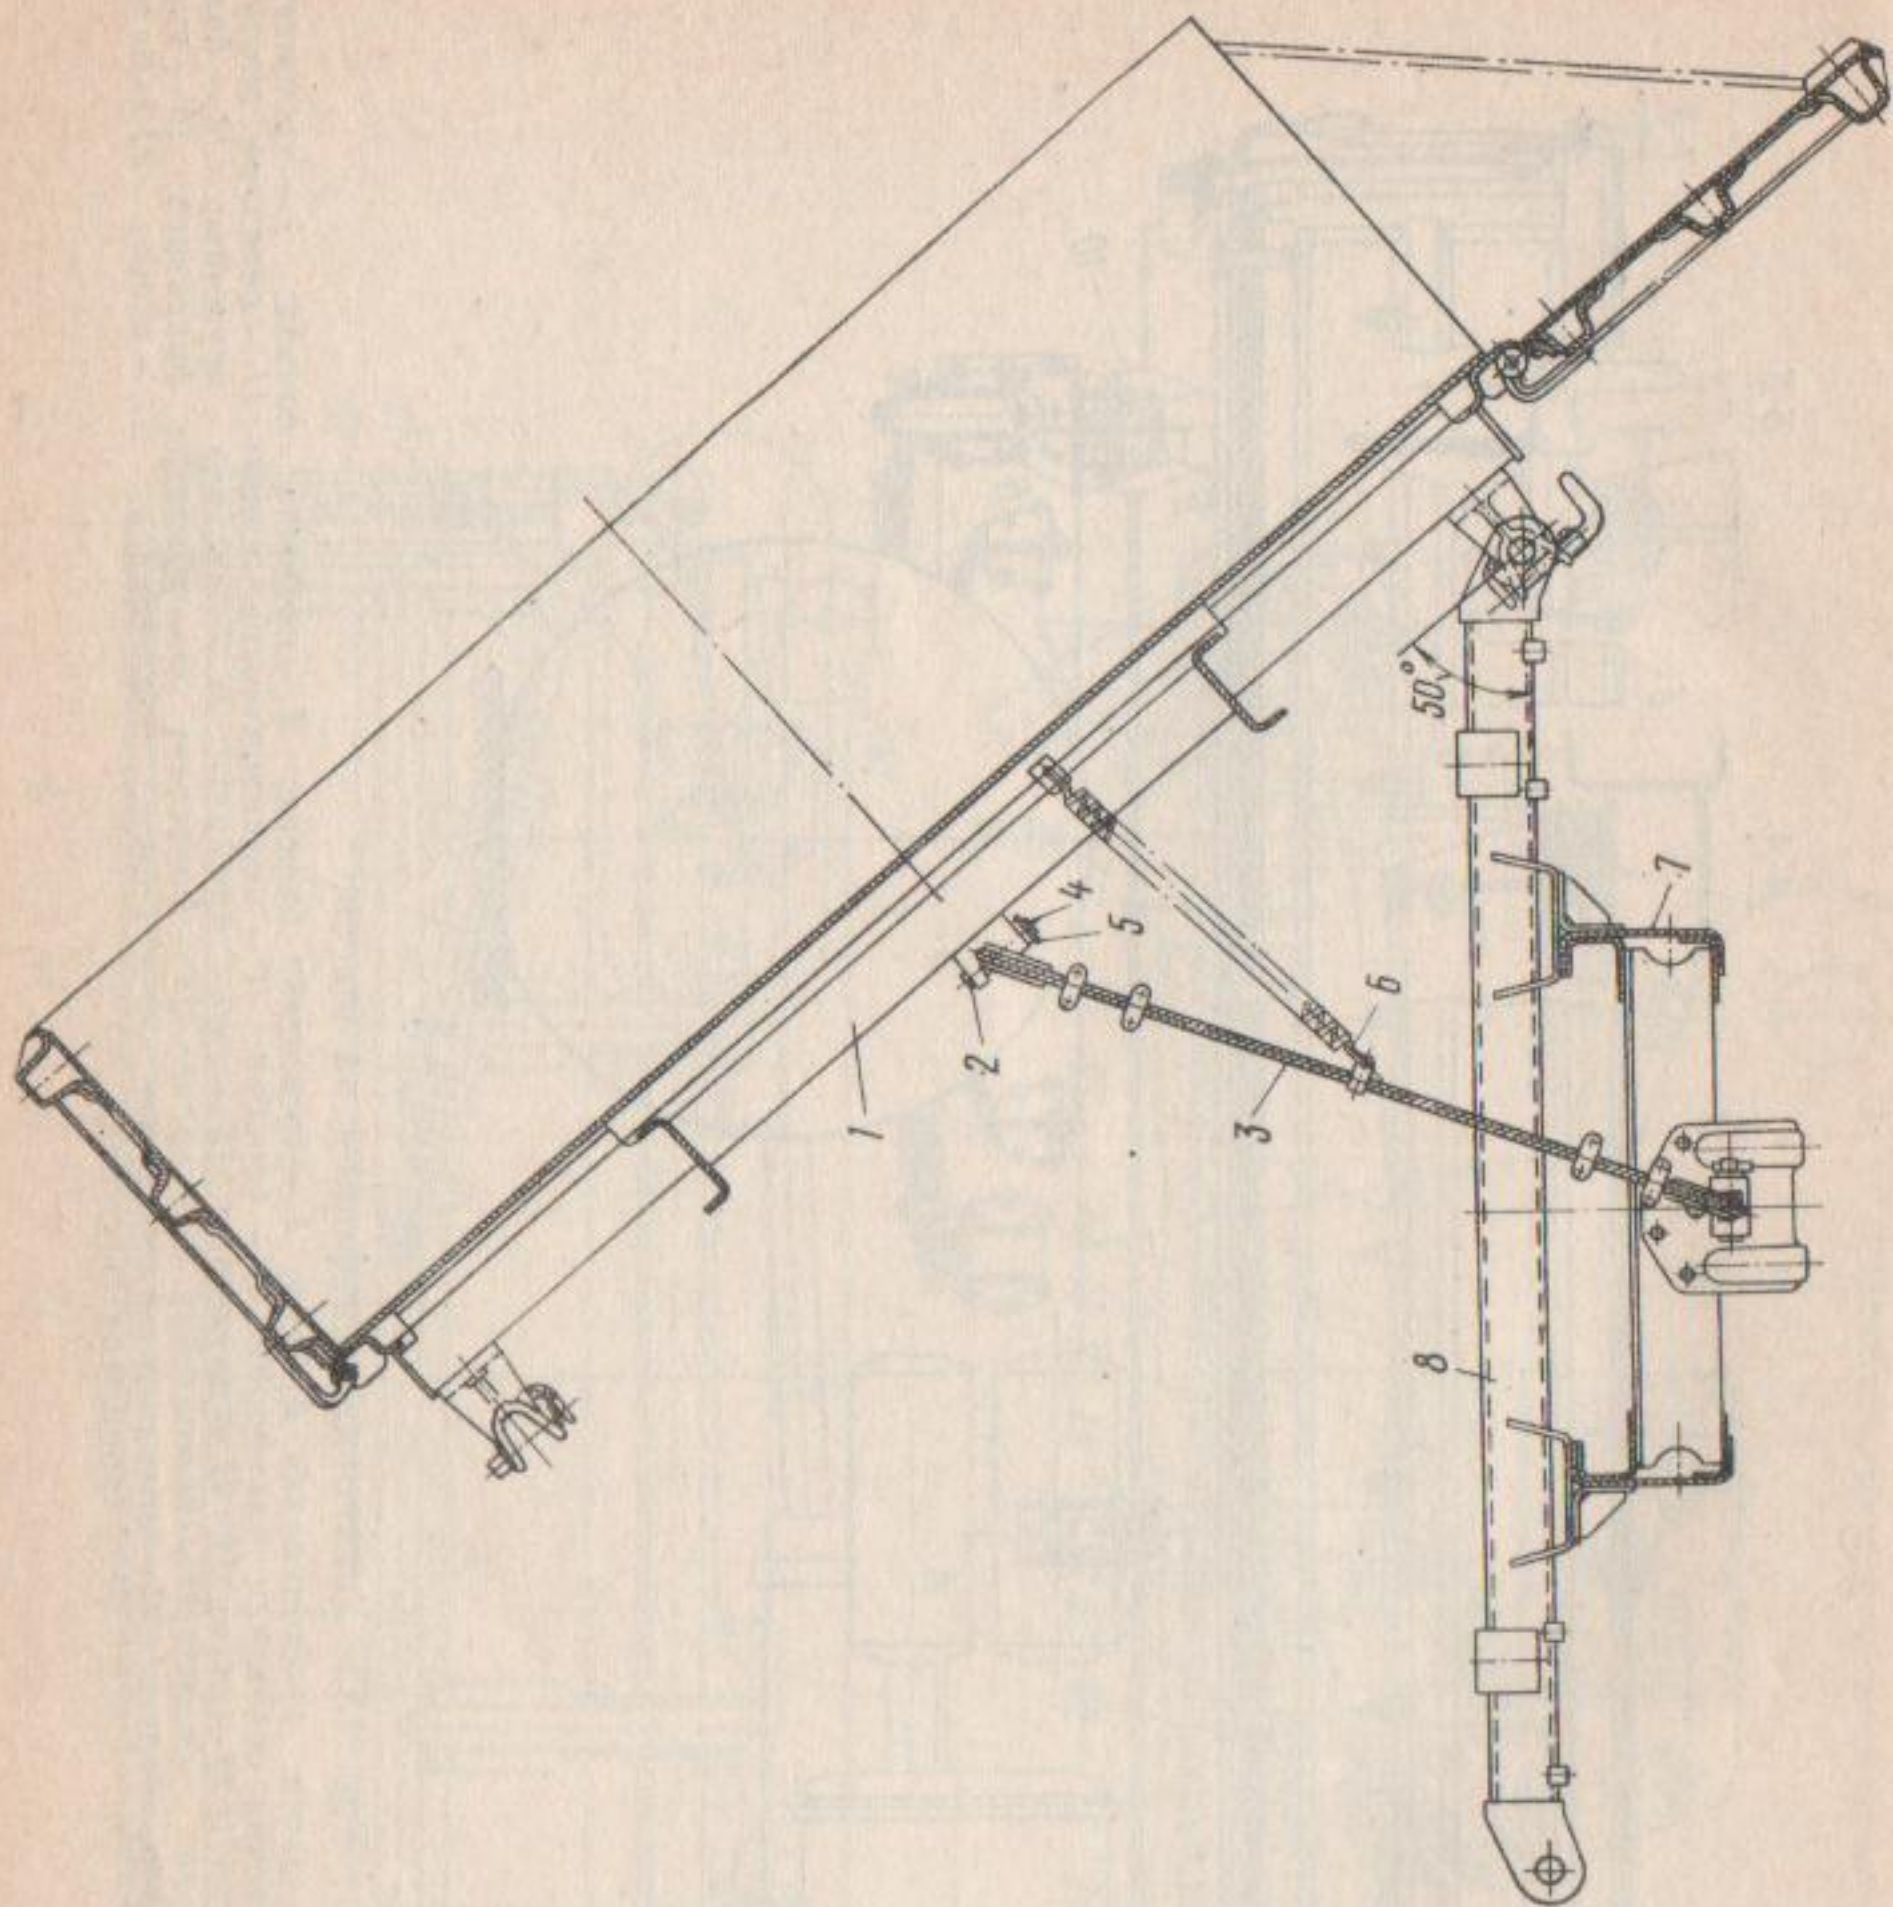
Установка страховочного троса ограничения подъема платформ:
